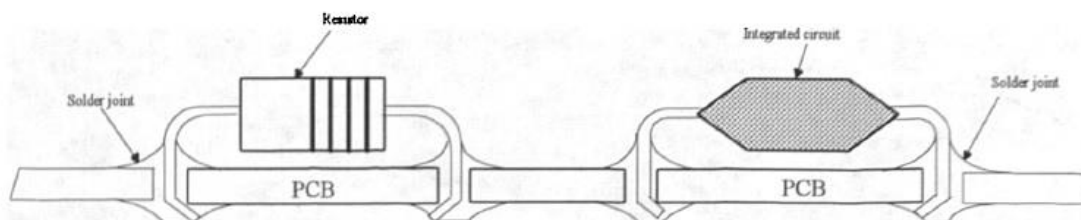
Juntas de solda da tecnologia *through-hole* in “Hui, *Analysis of surface mount technology solder joints*, 1996”
